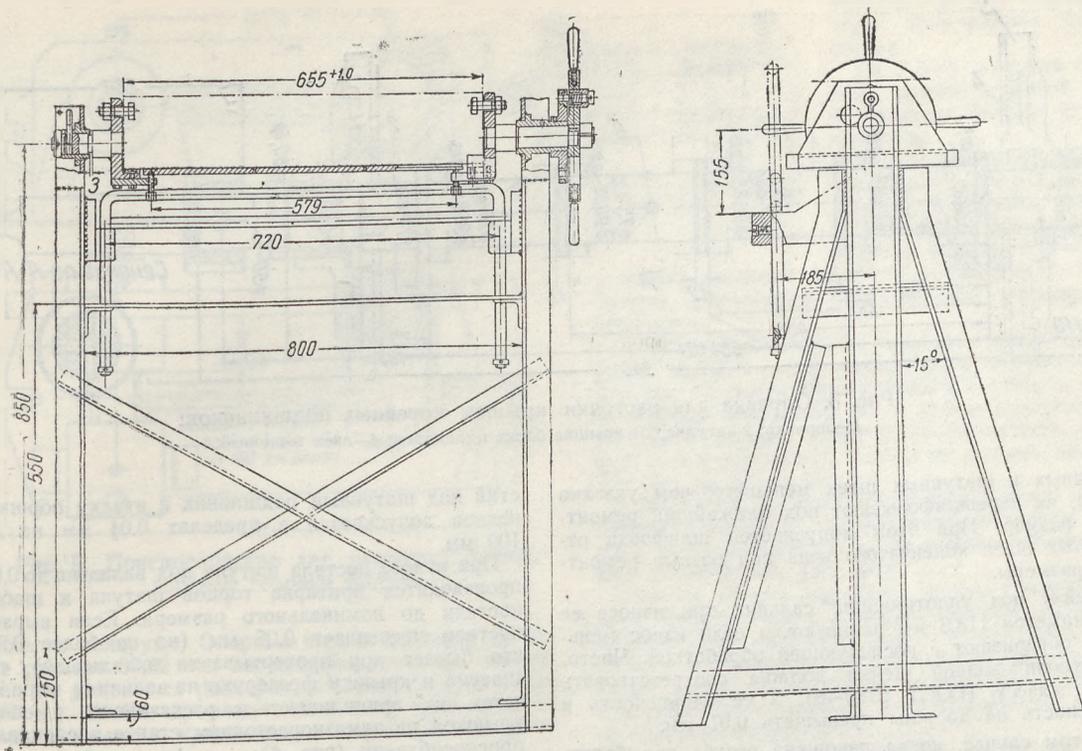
Стенд для разборки и сборки головки блока цилиндров.
